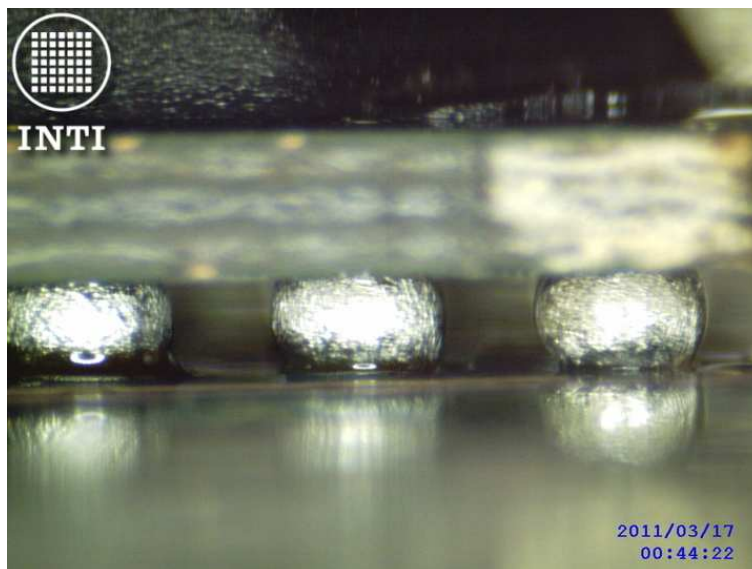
Detalle de las bolitas luego del proceso de soldadura.
